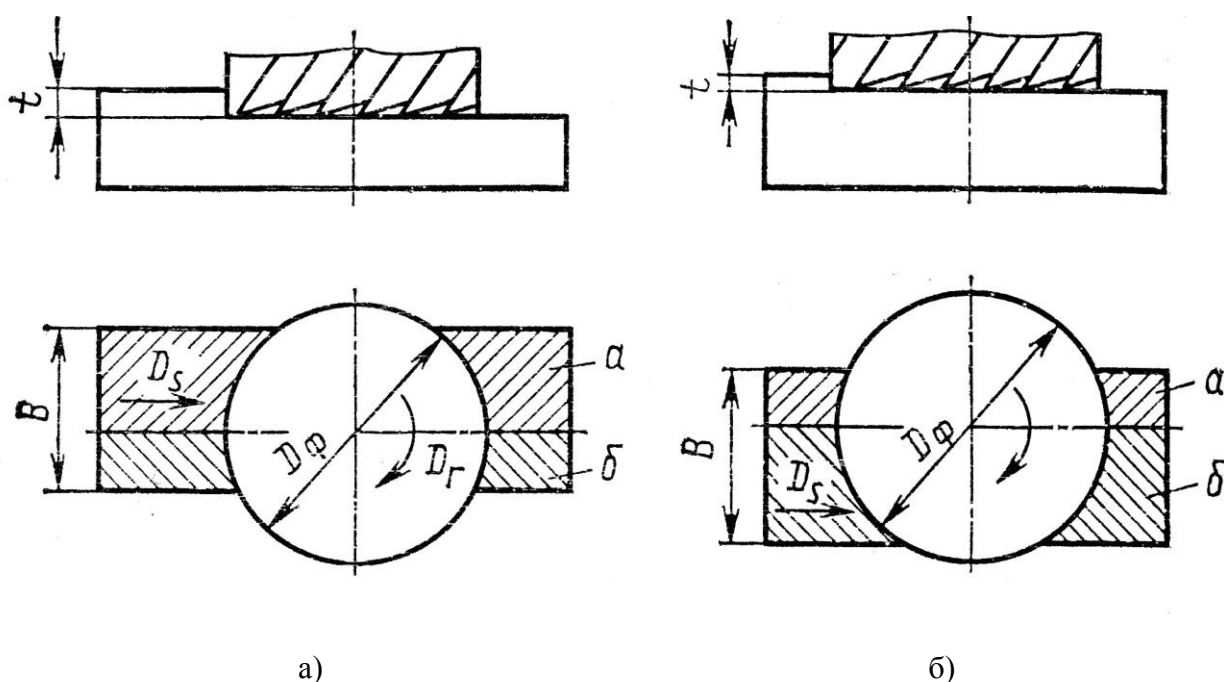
Попутное и встречное фрезерование торцовыми фрезами
